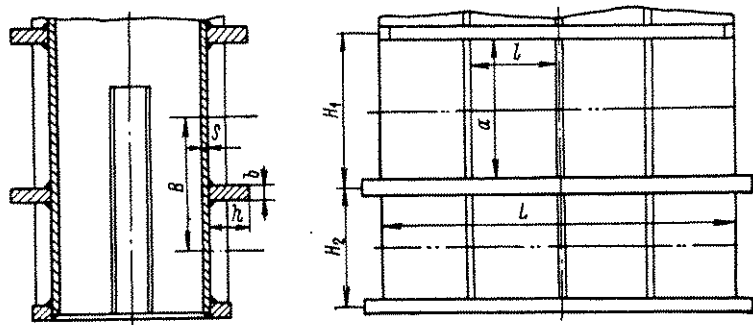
Сварная крышка (нижняя часть) задвижки большого диаметра прохода
